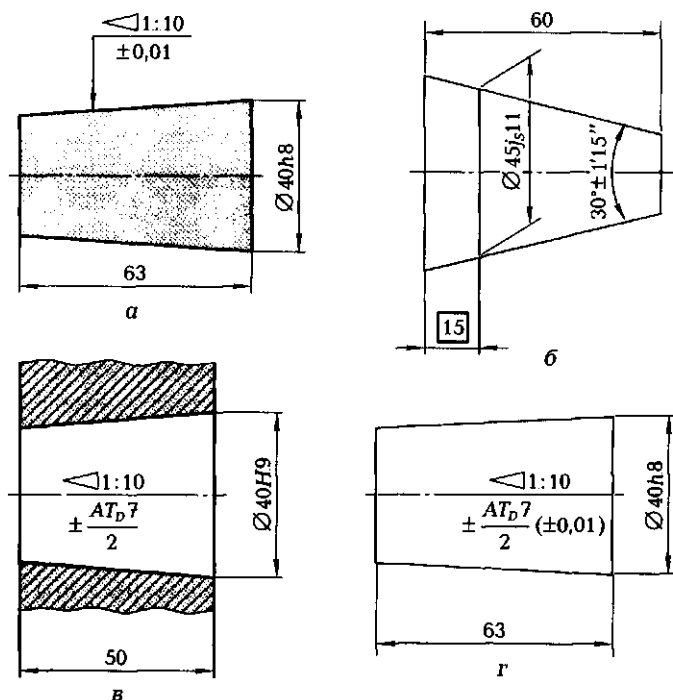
Способы обозначения допусков конусов на чертежах:
